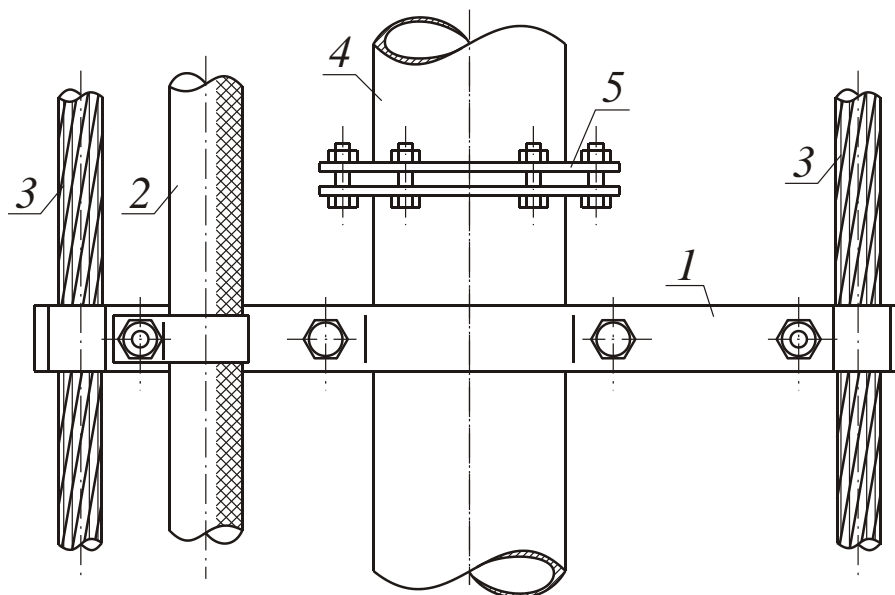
Конструкция хомута для подвески труб и кабеля подвесного проходческого насоса:
